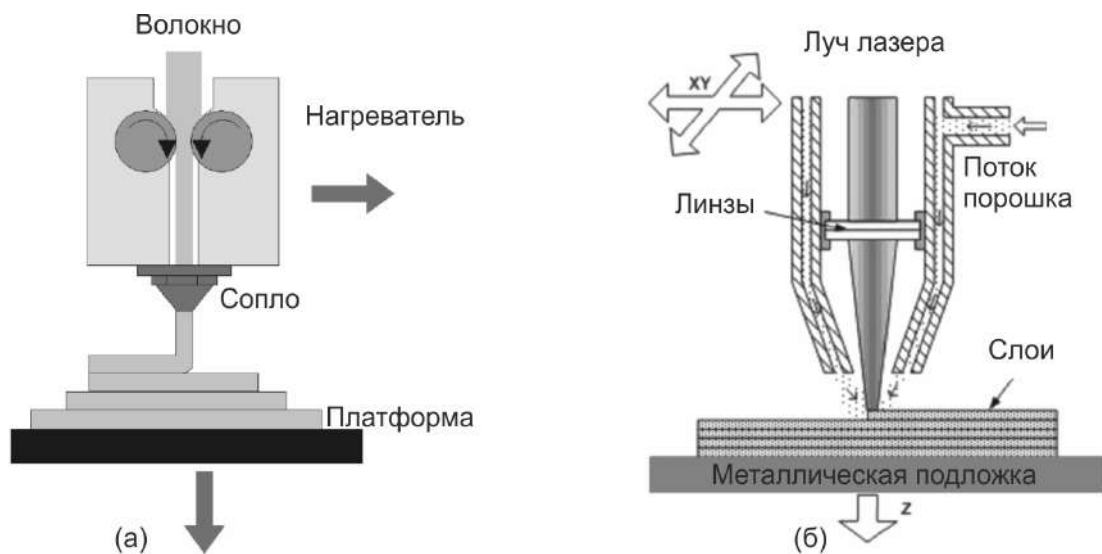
Схема процессов БИ: а – экструзия расплава; б – лазерная наплавка порошка [135].
